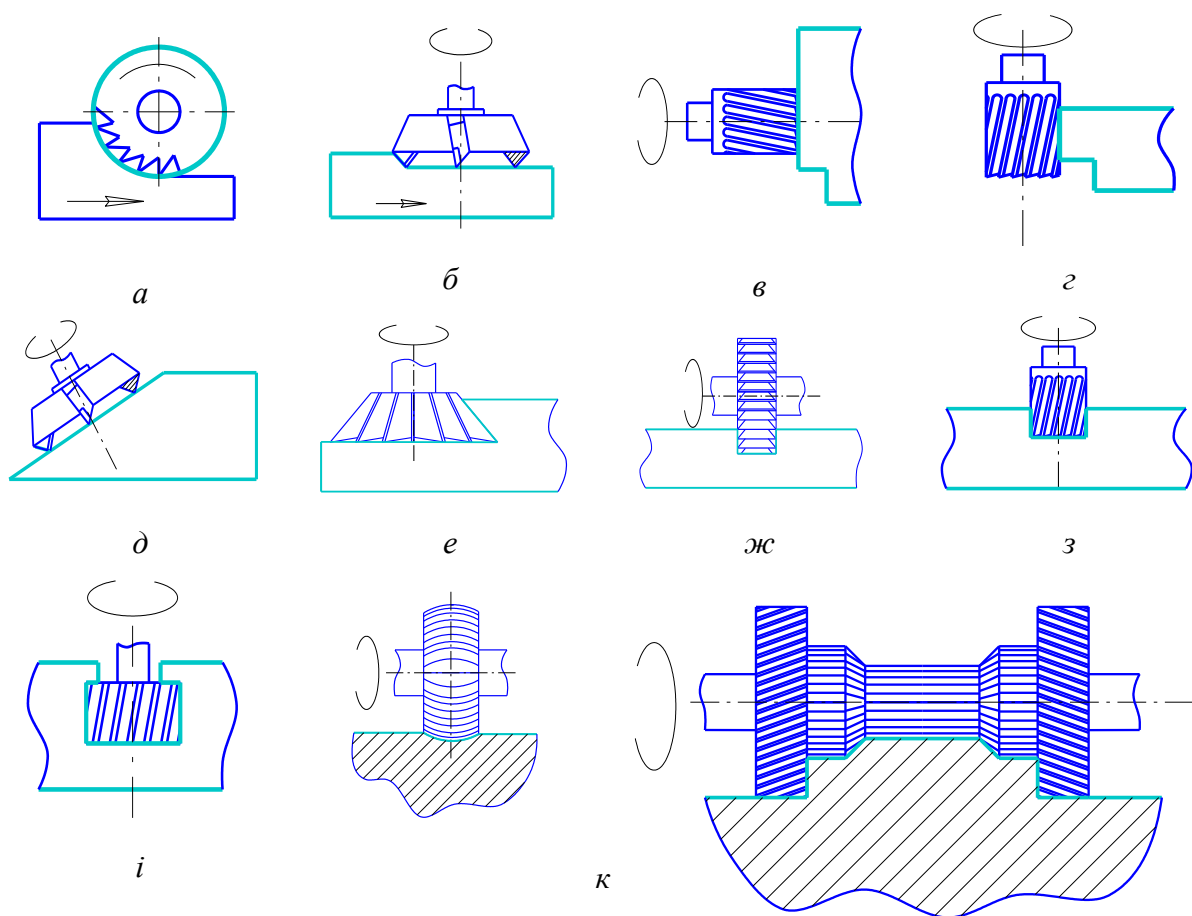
Основні види обробки, що виконуються на фрезерних верстатах
